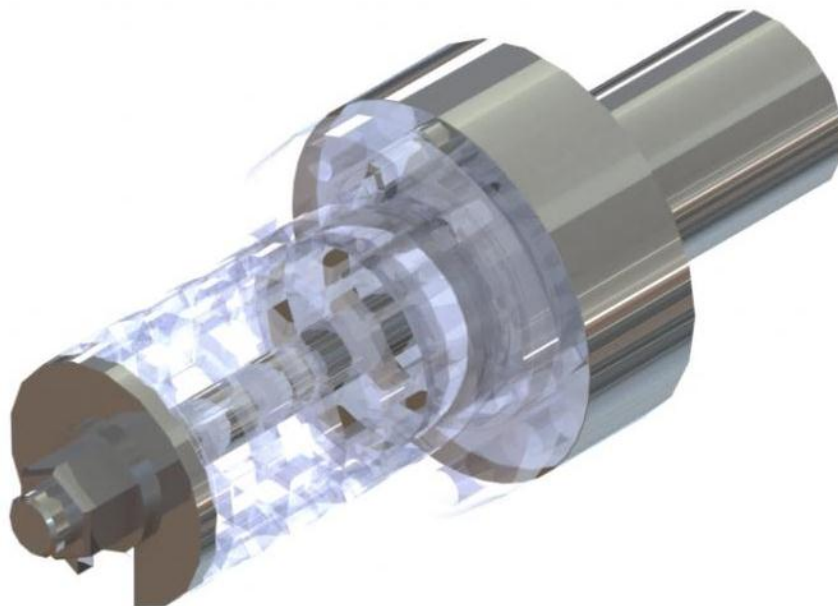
Трехмерная модель специального приспособления с установленной на него деталью
